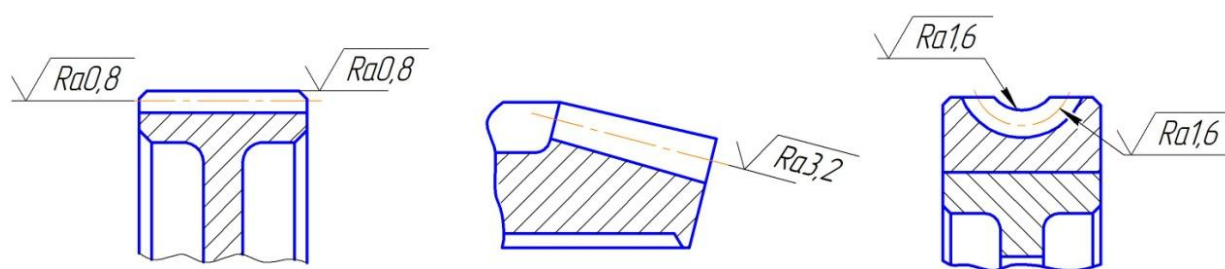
Обозначение шероховатости на зубчатых и червячных колесах
